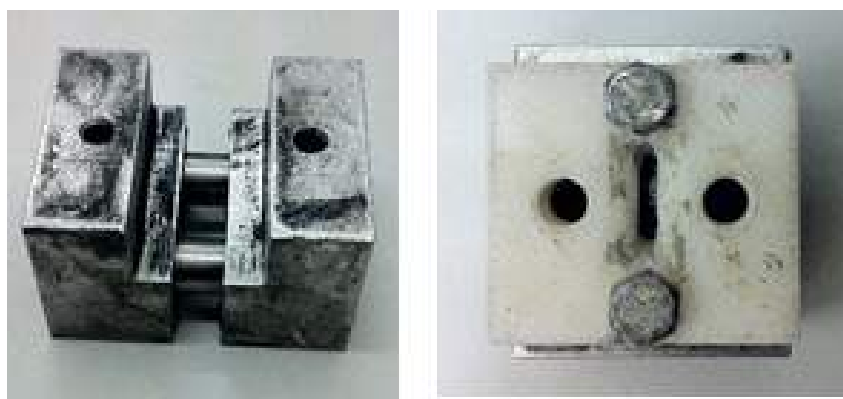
Moule utilisé pour la fabrication des échantillons.
